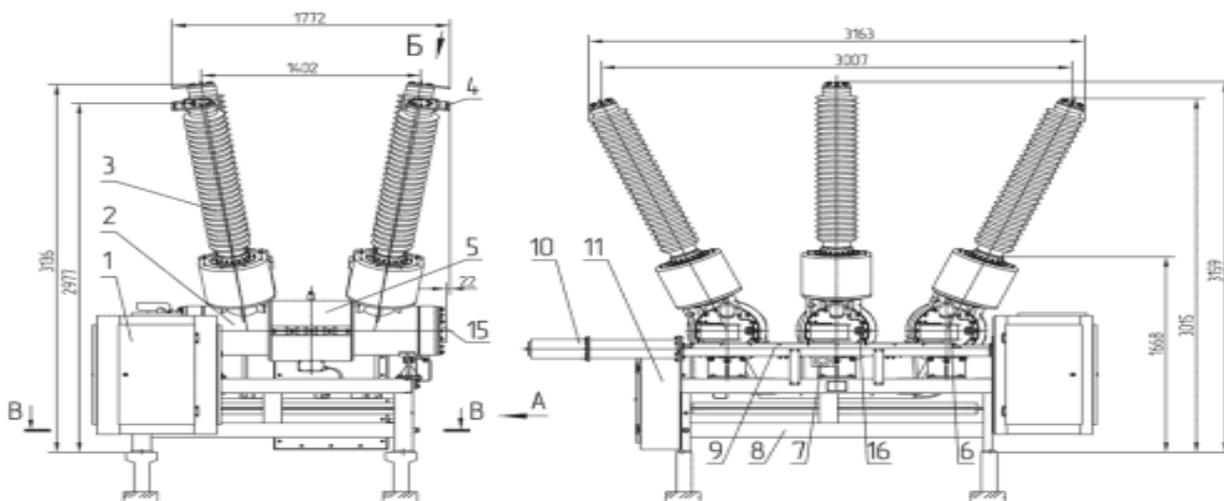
Общий вид и габаритно-установочные размеры выключателя ВЭБ-110П-40/2500 У1
